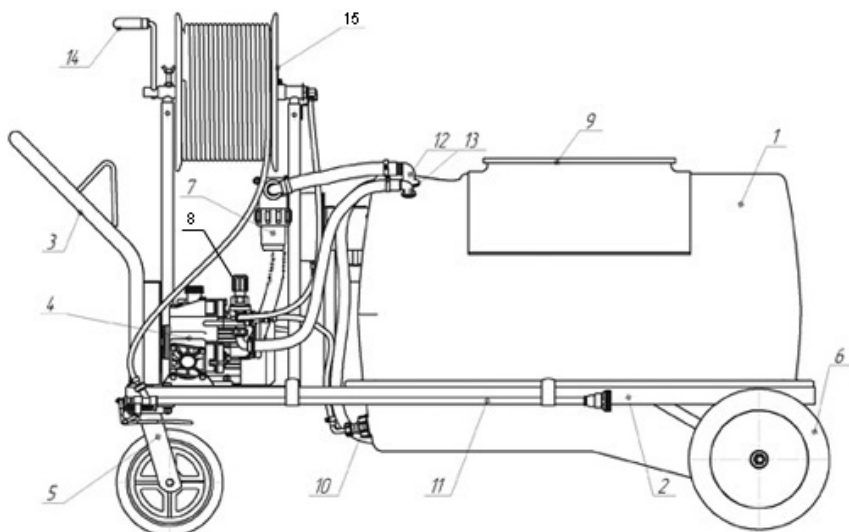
Опрыскиватель для теплиц: 1 – бак; 2 – рама; 3 – рукоятка; 4 – насос; 5 – поворотные колеса; 6 – опорные колеса; 7 – фильтр линии всасывания; 8 – регулятор давления; 9 – заливная горловина; 10 – гидромешалка; 11 – гидравлический пистолет; 12, 13 – фитинги; 14 – рукоятка; 15 – катушка для шланга
